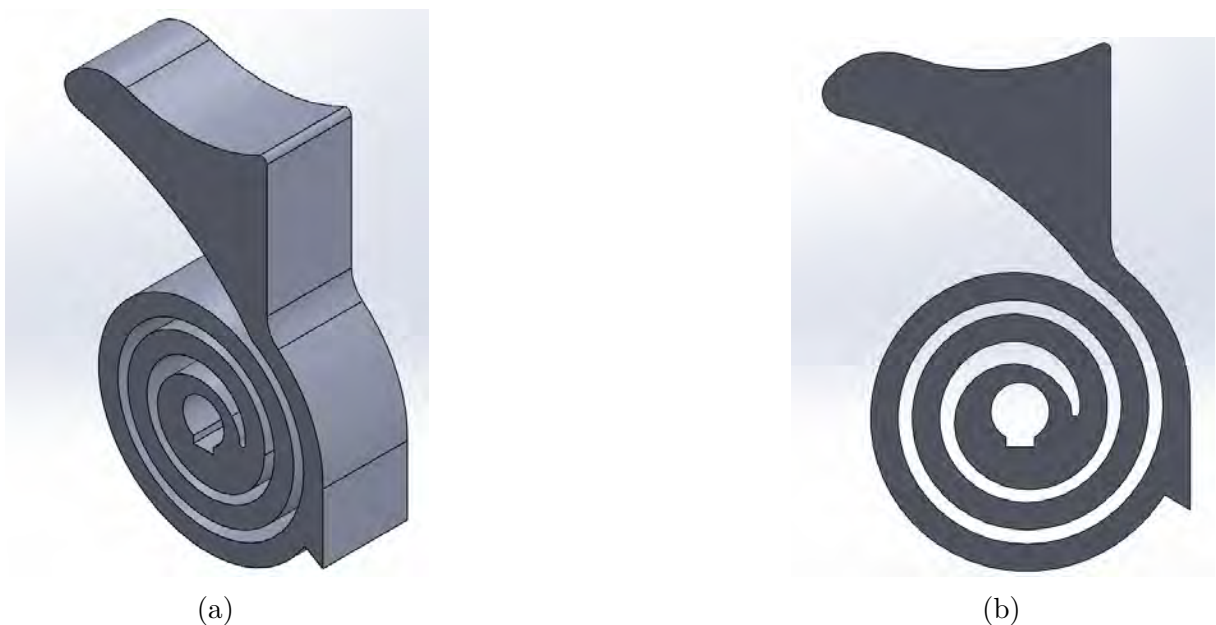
Desenho CAD do novo mecanismo proposto (a) - Vista isométrica (b) Vista frontal
